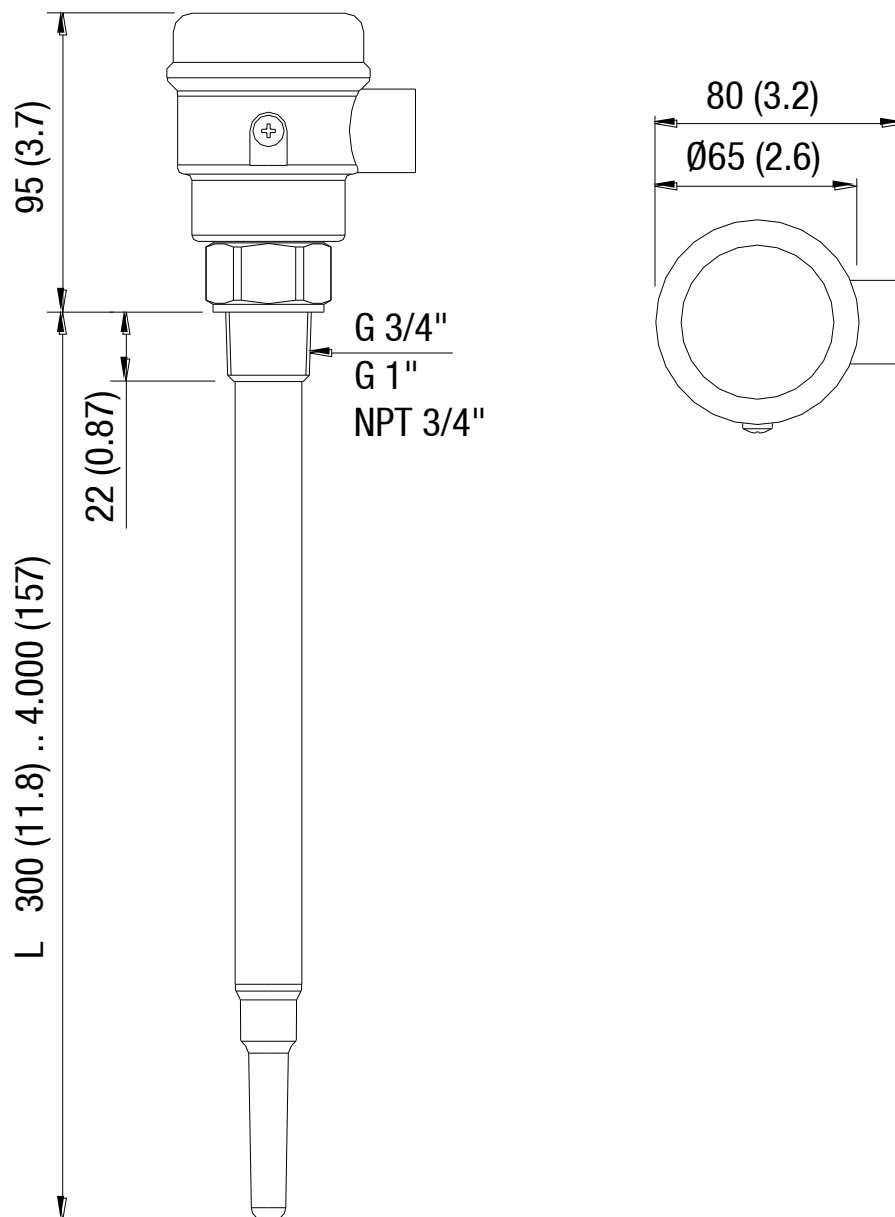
Abmessungen CN 7130, Gehäuse Ø 65 mm
